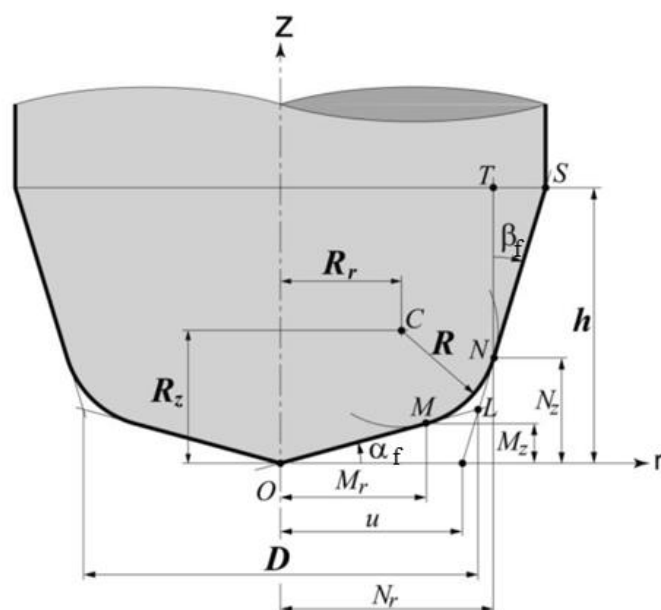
Geometria geral da fresa frontal, adaptado de [13].
